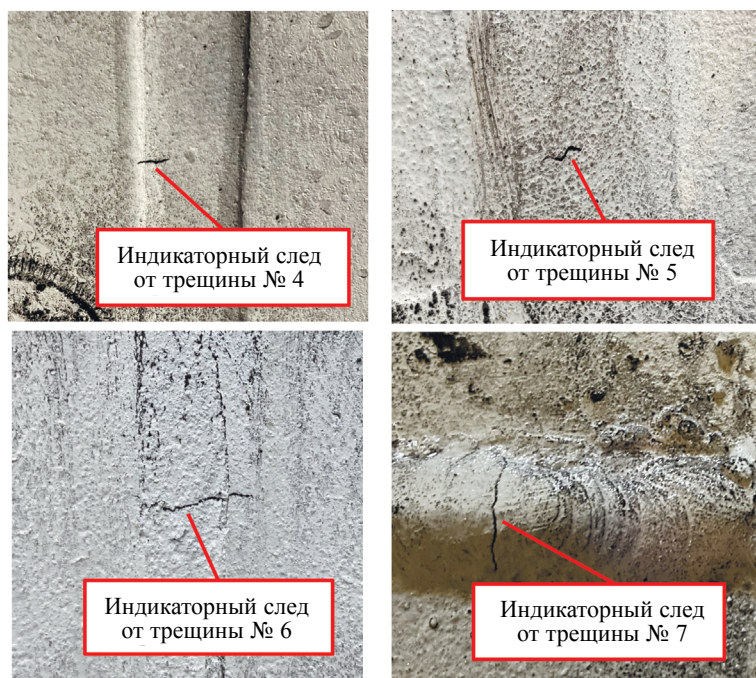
Поперечные трещины в сварных швах, выполненных полуавтоматической сваркой под флюсом (4—6) и ручной дуговой сваркой (7).
